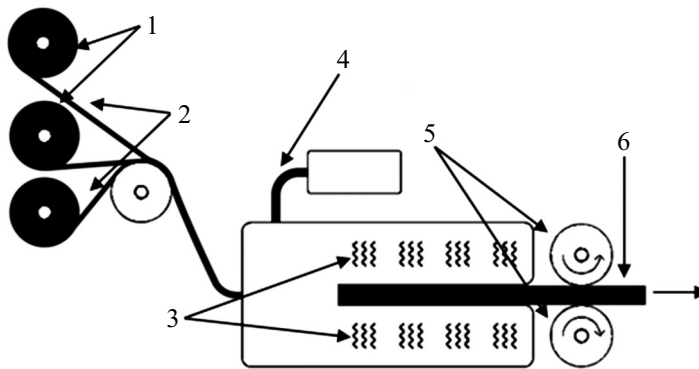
Изготовление композитов с натуральными волокнами методом пултрузии: 1 — катушки с прядями волокон; 2 — волокна; 3 — нагреватели; 4 — смола; 5 — эскалаторы с охлаждающей жидкостью; 6 — готовое изделие.
